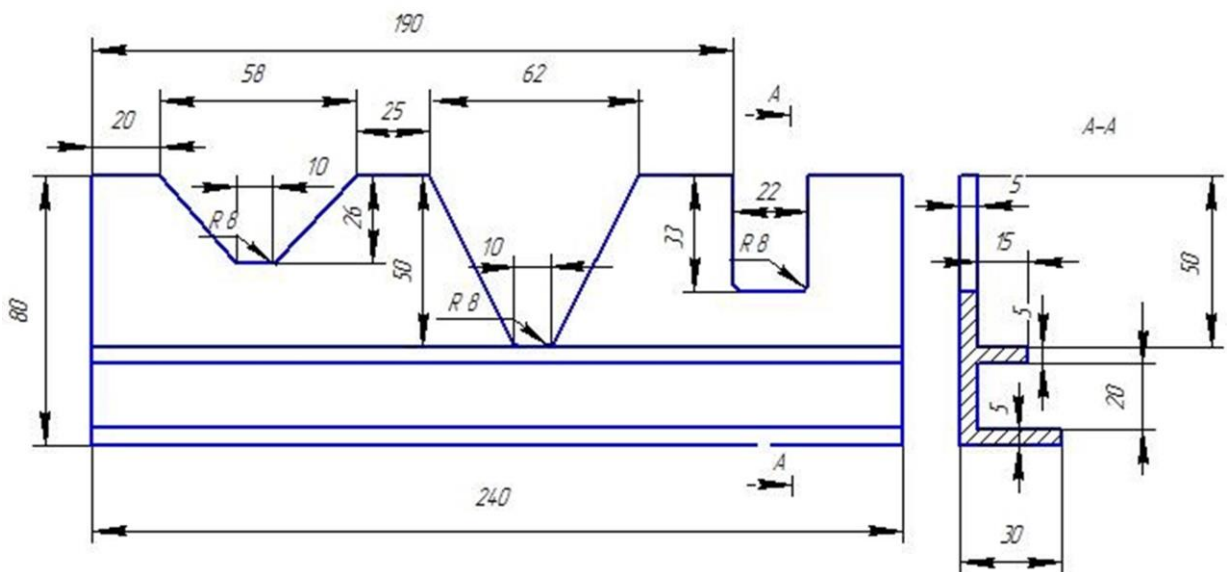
Эскиз 3 образца с различным сочетанием поверхностей
